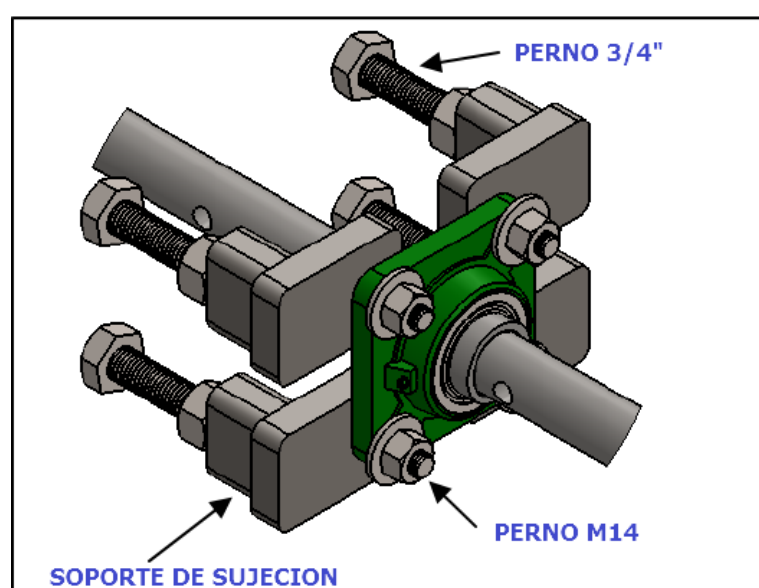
Vista del sistema de montaje de apoyo de fijación.
